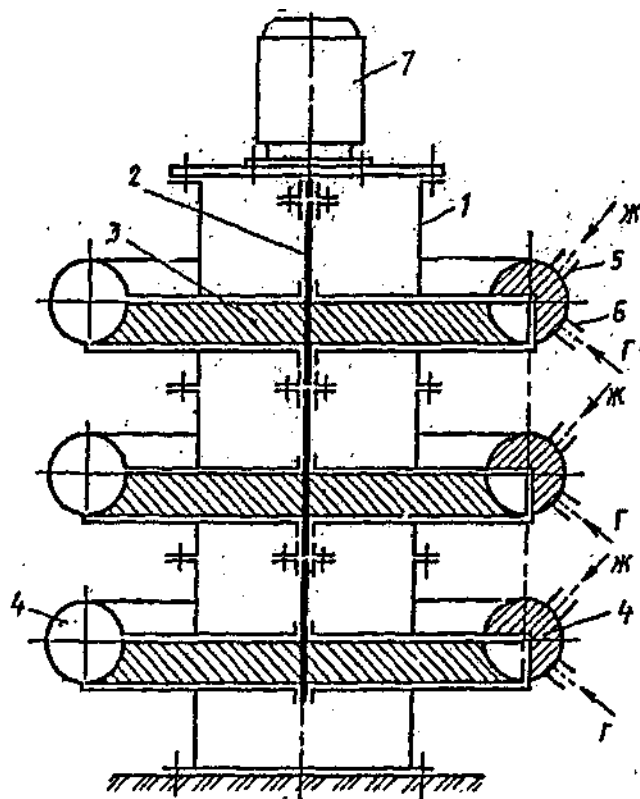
Роторный массообменный реактор: 1 – корпус; 2 – вал; 3 – диск; 4 – тороидальная камера; 5,6 – входные патрубки жидкости и газа; 7 – электродвигатель
